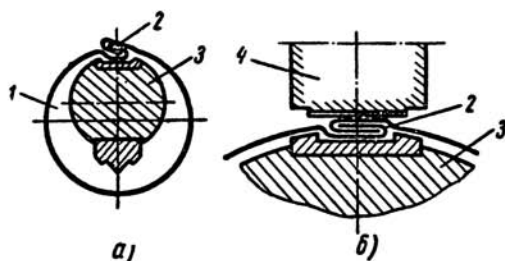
Схема установки лежащего фальца (а) и закатка его на станке ВМС-64 (б)
